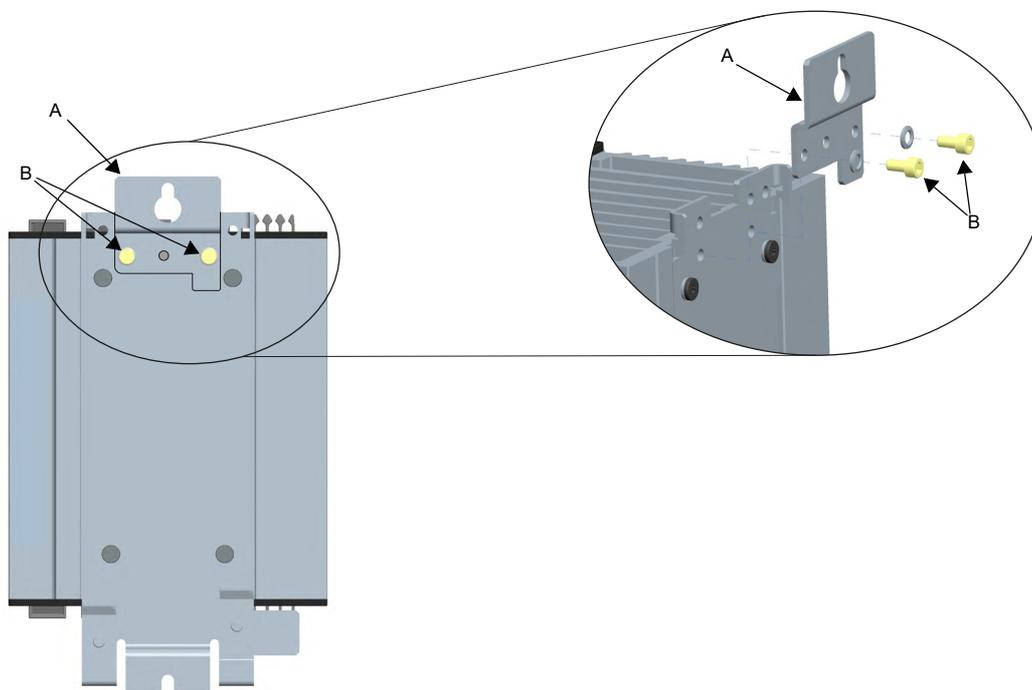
Befestigen der oberen Halterung für die Rückwand-Lochmontage
